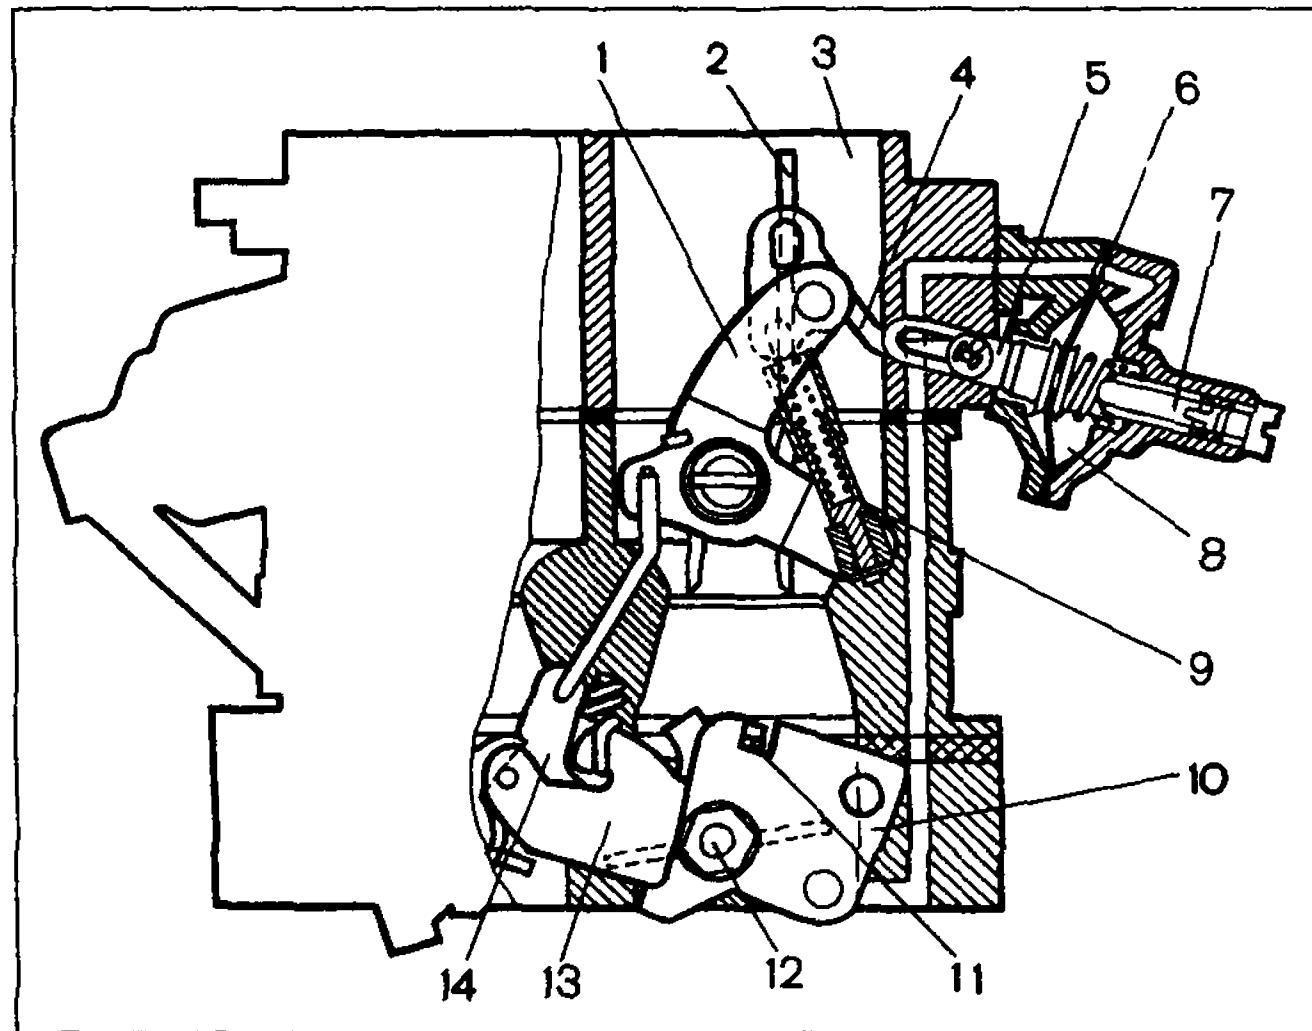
Схема пускового устройства карбюратора 2107-1107010: 1 - рычаг управления воздушной заслонкой; 2 - воздушная заслонка; 3 - воздушный патрубок первой камеры; 4 - тяга; 5 - шток пускового устройства; 6 - диафрагма; 7 - регулировочный винт; 8 - полость, сообщающаяся с задрессельным пространством; 9 - телескопическая тяга; 10 - рычаг привода дроссельных заслонок; 11 - сектор (усик); 12 - ось дроссельной заслонки первой камеры; 13 - рычаг на оси дроссельной заслонки первой камеры; 14 - рычаг, связанный с воздушной заслонкой
